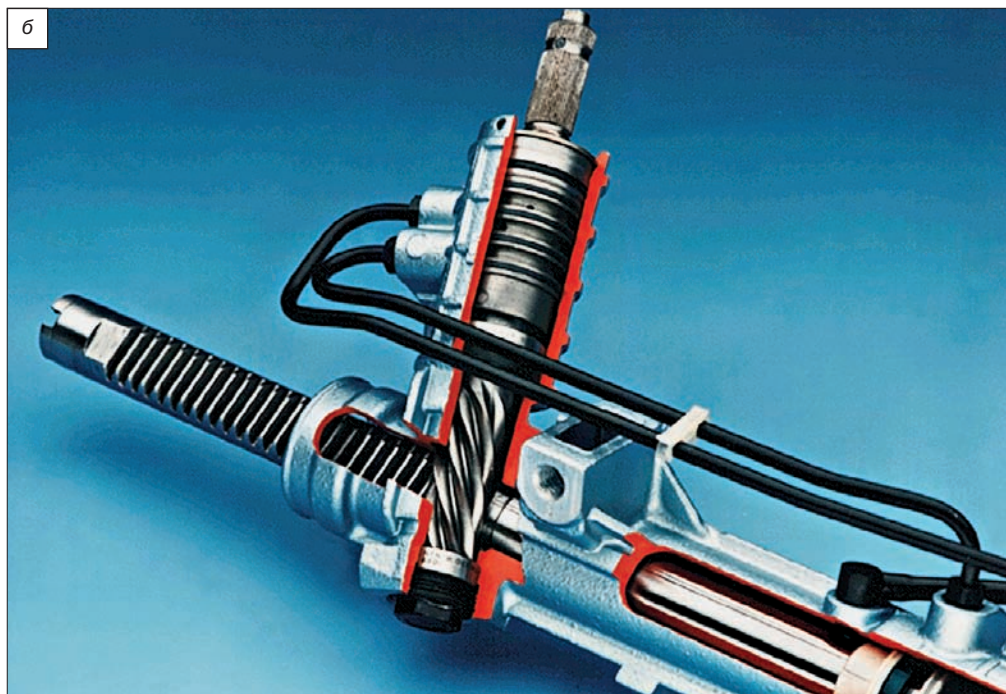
б, в. Реечный рулевой механизм с гидроусилителем: 1 — жидкость под высоким давлением; 2 — поршень; 3 — жидкость под низким давлением; 4 — шестерня; 5 — рулевая рейка; 6 — распределитель гидроусилителя; 7 — рулевая колонка; 8 — насос гидроусилителя; 9 — резервуар для жидкости; 10 — элемент подвески
